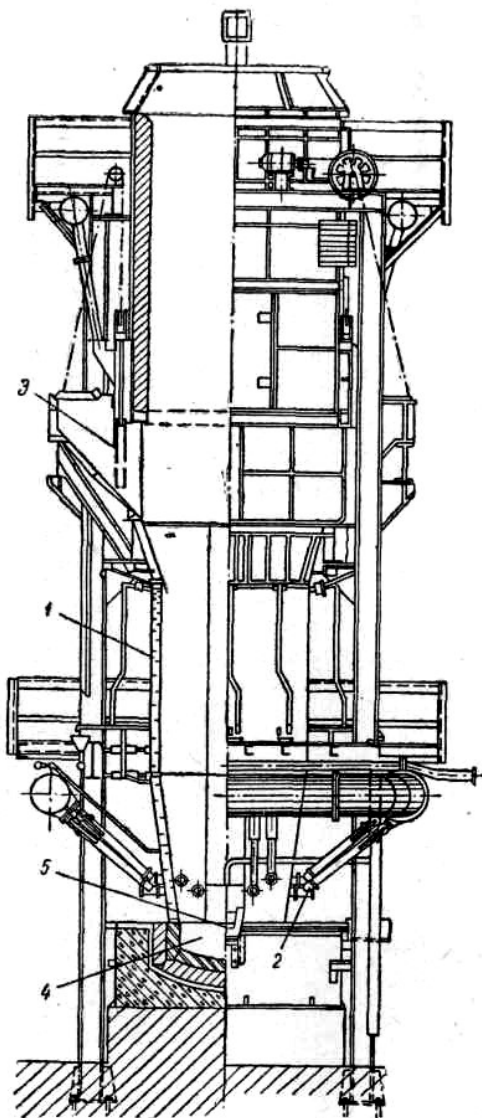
Шахтная печь для свинцовой плавки: 1—кессоны; 2—фурмы; 3—загрузочные окна; 4—горн; 5—летка для выпуска штейна и шлака
